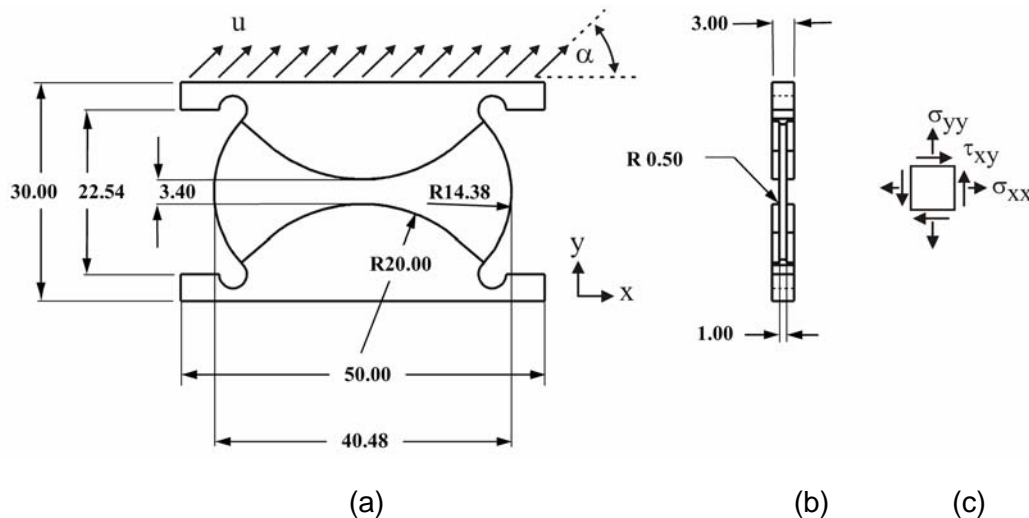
Technische Zeichnung der verwendeten Probengeometrie (a) Draufsicht, (b) Seitenansicht, (c) Spannungszustand im Prüfbereich
